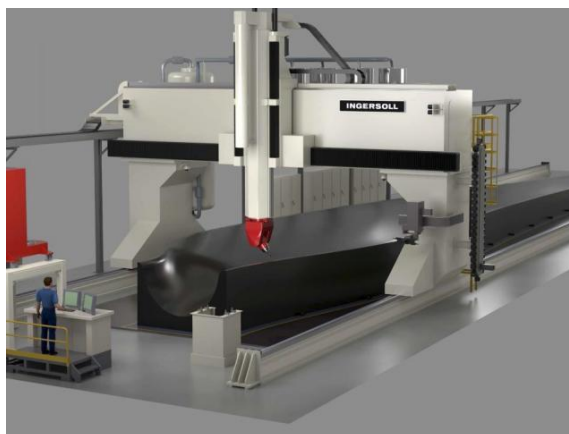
fotografía del sistema de impresión WHAM – Fuente: [additivemanufacturing.media](http://additivemanufacturing.media)
